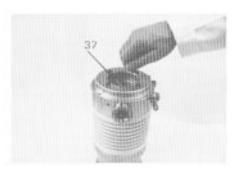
Spritzmutter 37 herausdrehen Unscrew splash nut 37 Dévisser l'écrou de barbotage 37
